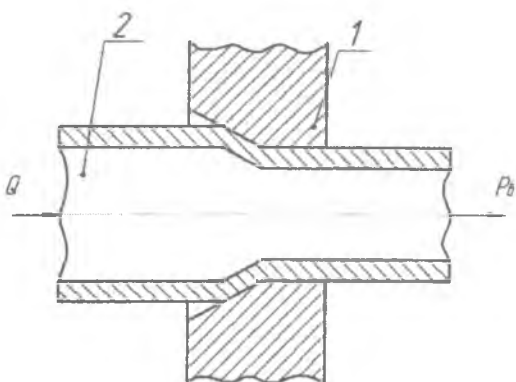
Схема волочения трубы с осевым подпором: 1 – волока; 2 – трубная заготовка.
